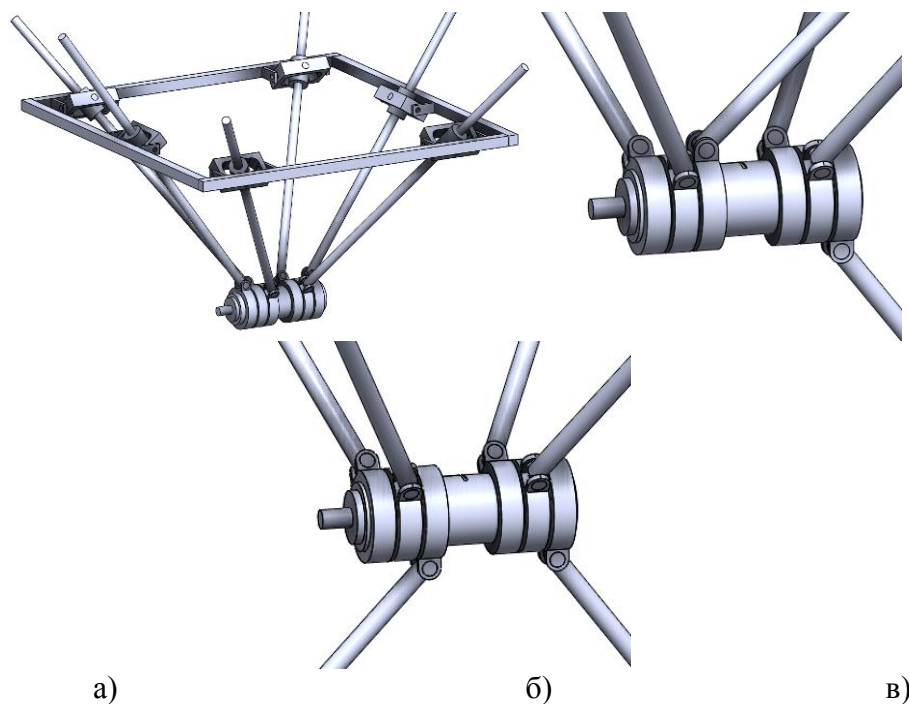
Багатокоординатний верстат з надлишковим приводом:
